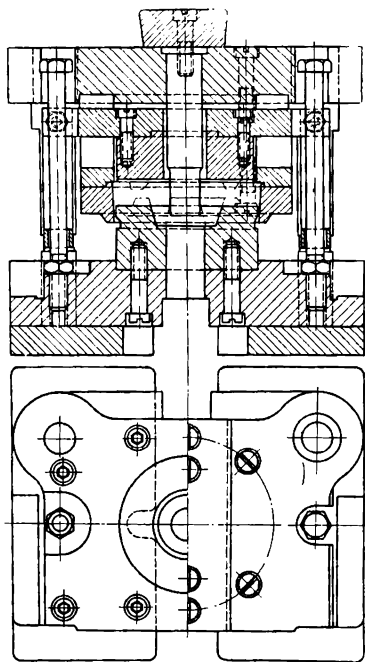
Совмещенный штамп для обрезки и прошивки при малом диаметре прошиваемой перемычки
